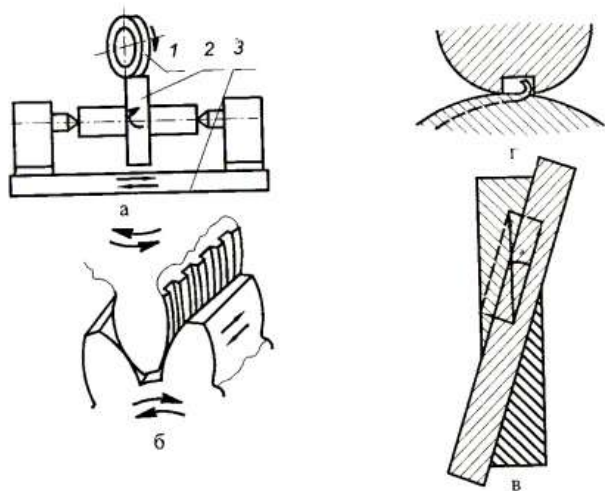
Схема шевінгування зубчастих коліс:
